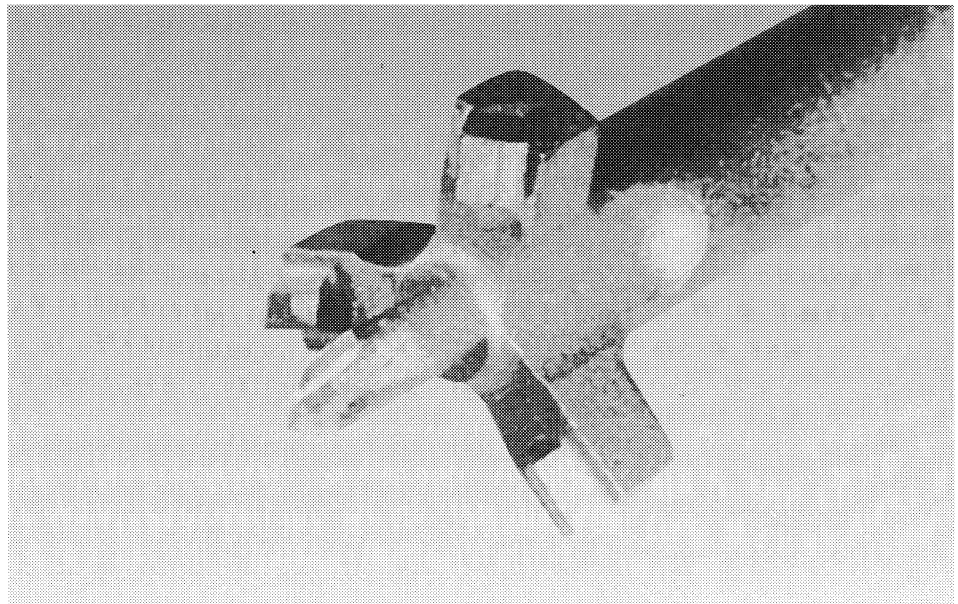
Prototypenwerkzeuge mit Durchmesser 25 mm
